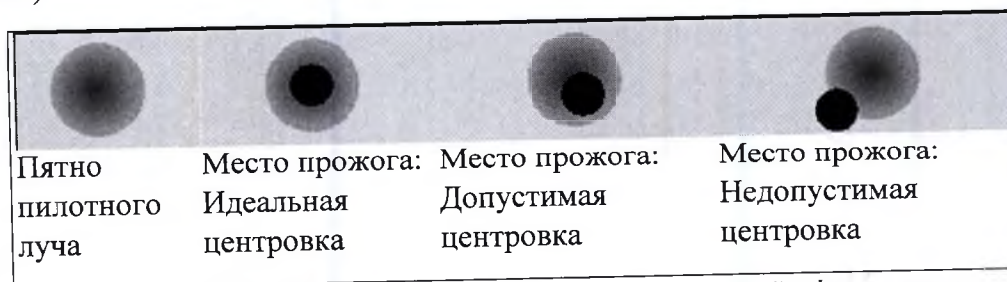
Проверка центровки лазерного луча – стандартный сфокусированный излучатель
